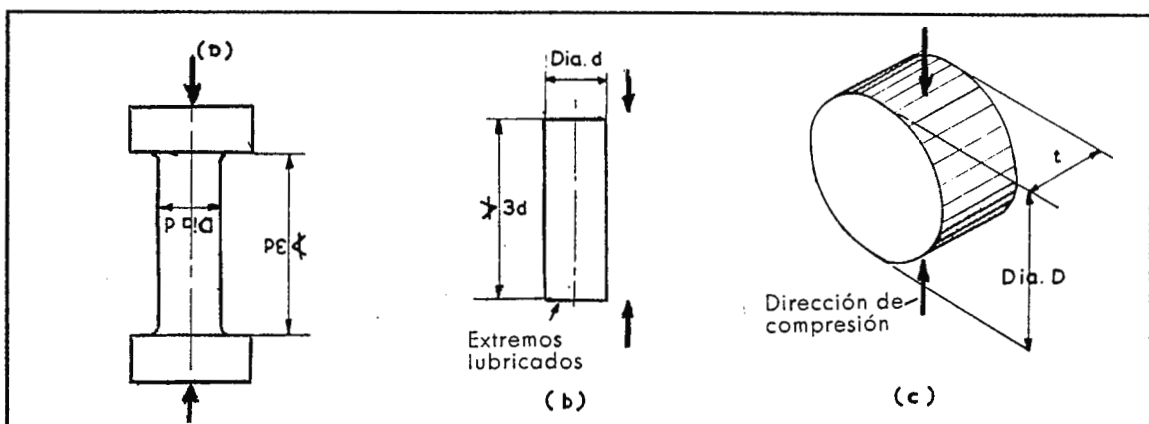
Probetas de compresión: (a) Diseño inaceptable, incluso con límites de medida normales. (b) Probeta de compresión aceptable. (c) Probeta de compresión diametral, para material frágil.
